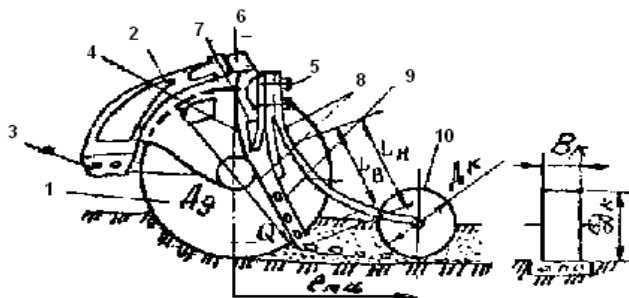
Схема двухдискового сошника с распределителем для ленточного высева семян: 1 – диск рабочий; 2 – корпус; 3 – поводок; 4 – распределитель семян; 5 – болты крепления; 6 – горловина; 7 – отражатель; 8 – распределительная пластина; 9 – верхняя пластина; 10 – каток прикатывающий
